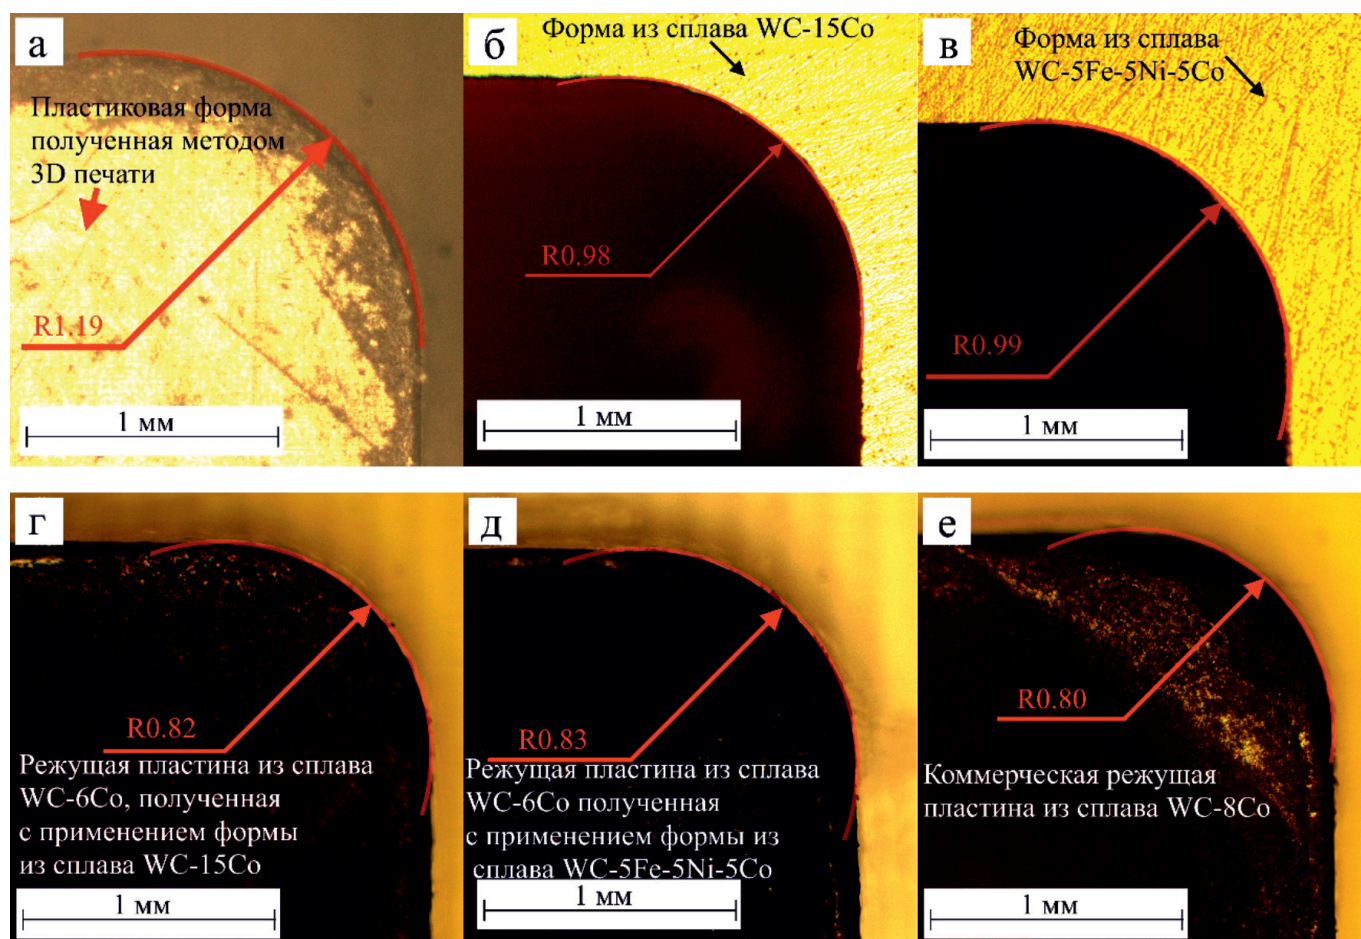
Фотографии скругления пластиковой матрицы для прессования заготовки пресс-формы, полученной методом 3D-печати (а), фотографии матриц пресс-форм для прессования заготовок режущих пластин, изготовленных из сплава WC-15Co (б) и WC-5Fe-5Ni-5Co (в), скругление изготовленных режущих пластин (г, д), скругление коммерческой режущей пластины (е)
